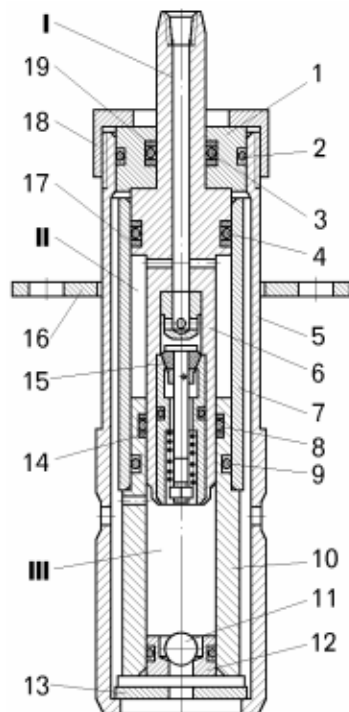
Приспособление для разборки и сборки цилиндров пневмогидравлической подвески:
